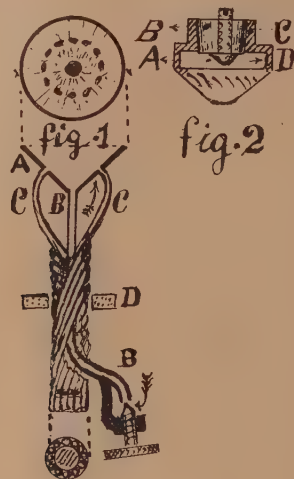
A, stator conique de 90° d'angle; B, conduit permettant par vis-pointeau le réglage d'arrivée d'air; C, tuyère; D, anneau de caoutchouc mousse. — Fig. 2 : A, vis du couvercle du rotor; B, couvercle du rotor; C, paroi cylindrique du rotor; D, gorge dans la cavité du rotor.
